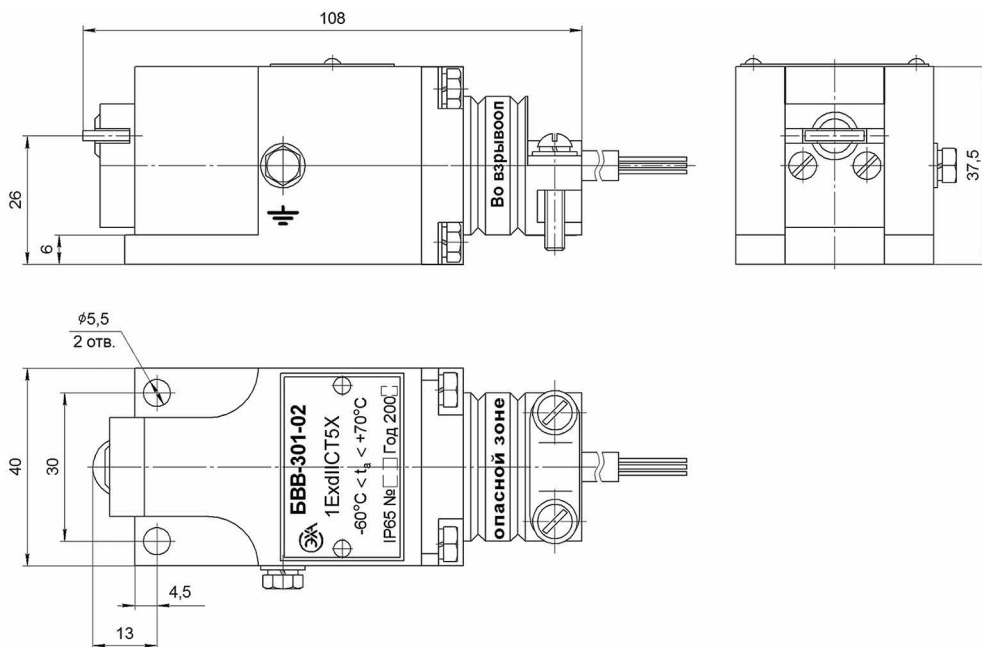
Габаритные и установочные размеры блока выключателей БВВ-301-02
